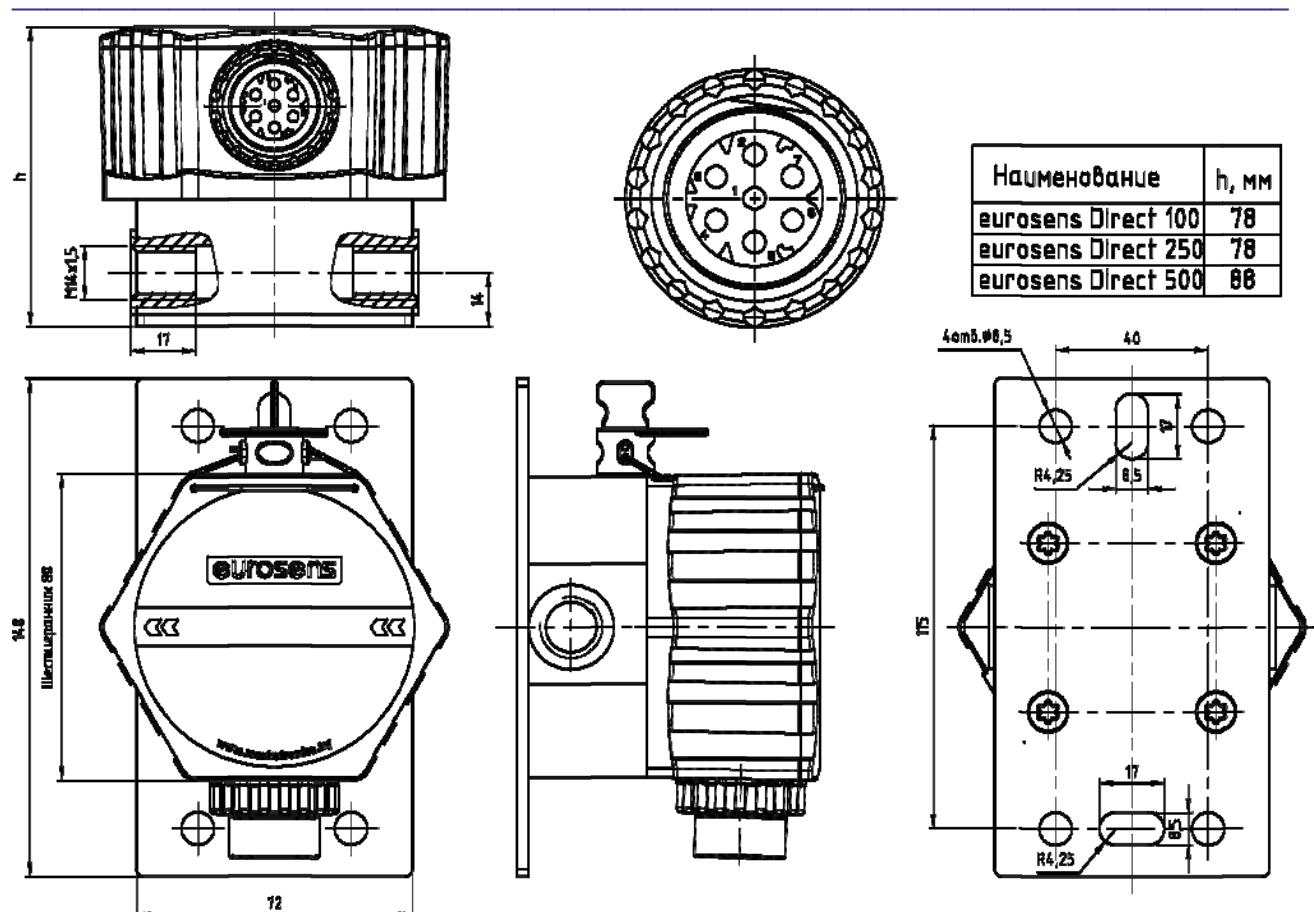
Габаритные и установочные размеры *EUROSENS Direct
